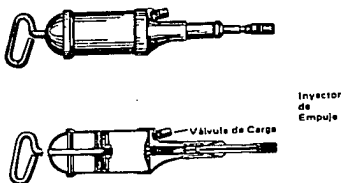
Pistolas de engrasar. a) De palanca b) De pistón.
